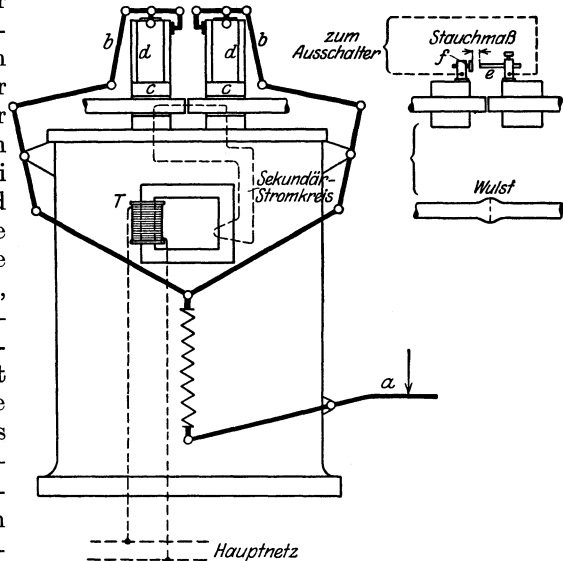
Schema einer Stumpfschweißmaschine.
